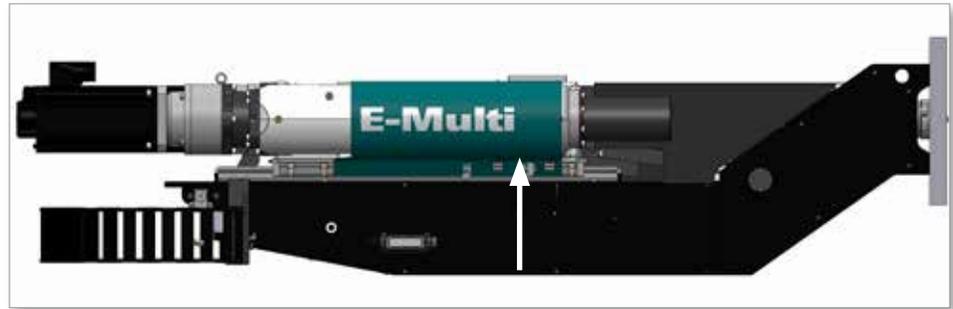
Seitenansicht mit Position der Schmierpunkte der Kugelgewindespindel
